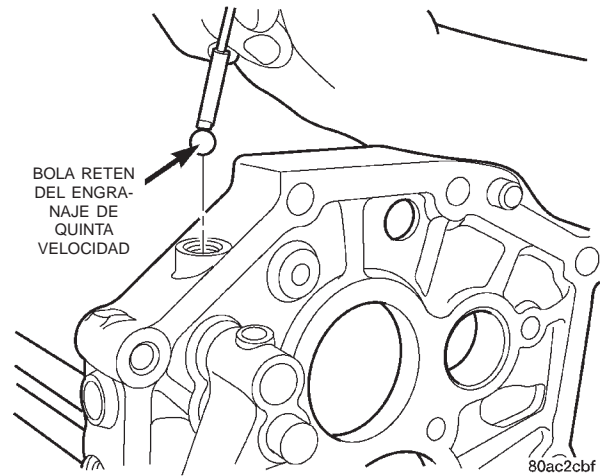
Instalación de la bola retén del engranaje de quinta velocidad
